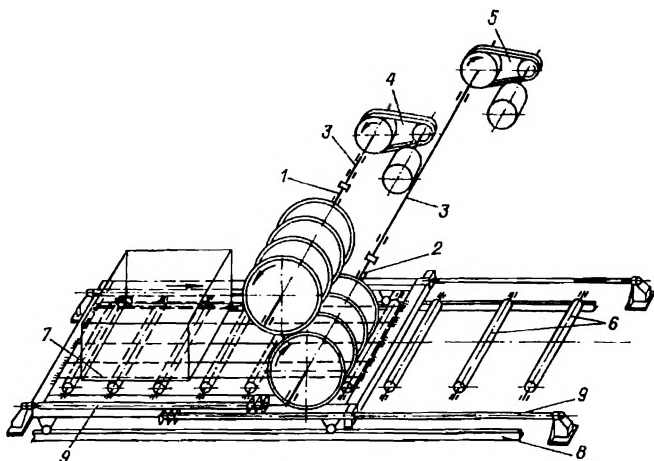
Кинематическая схема распиловочного многодискового двухвального станка модели SMP-017
